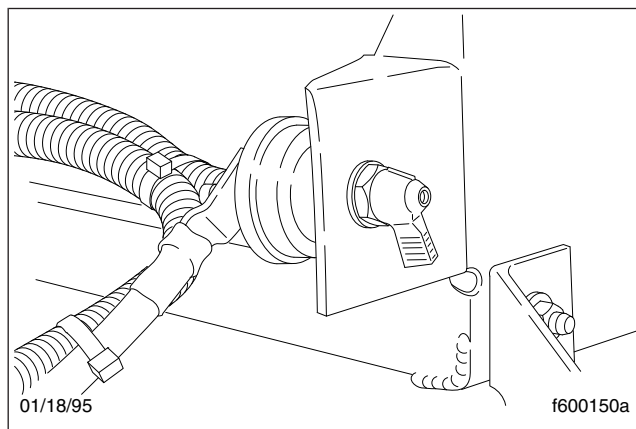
, Interruptor aislador de la cabina (de las baterías)
